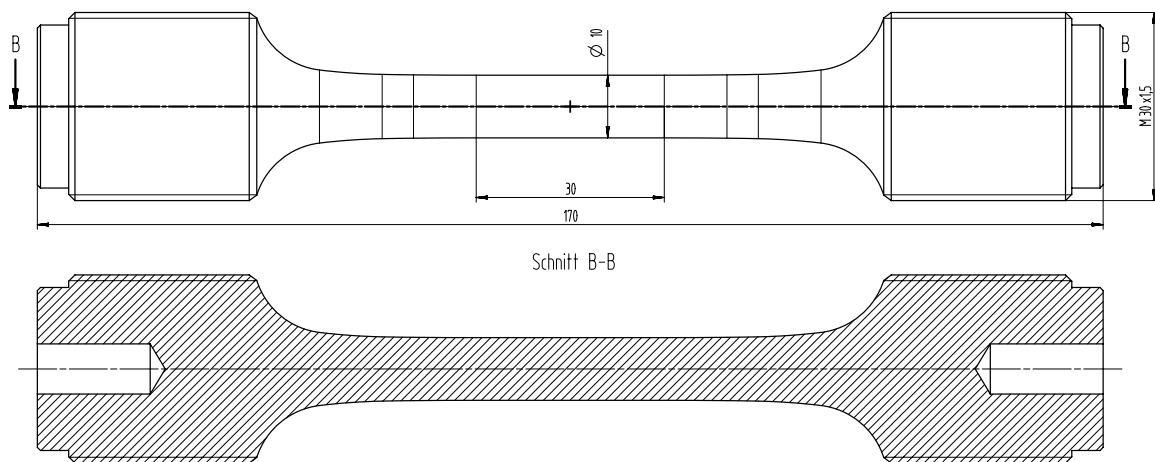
Fertigungszeichnung der Probengeometrie
